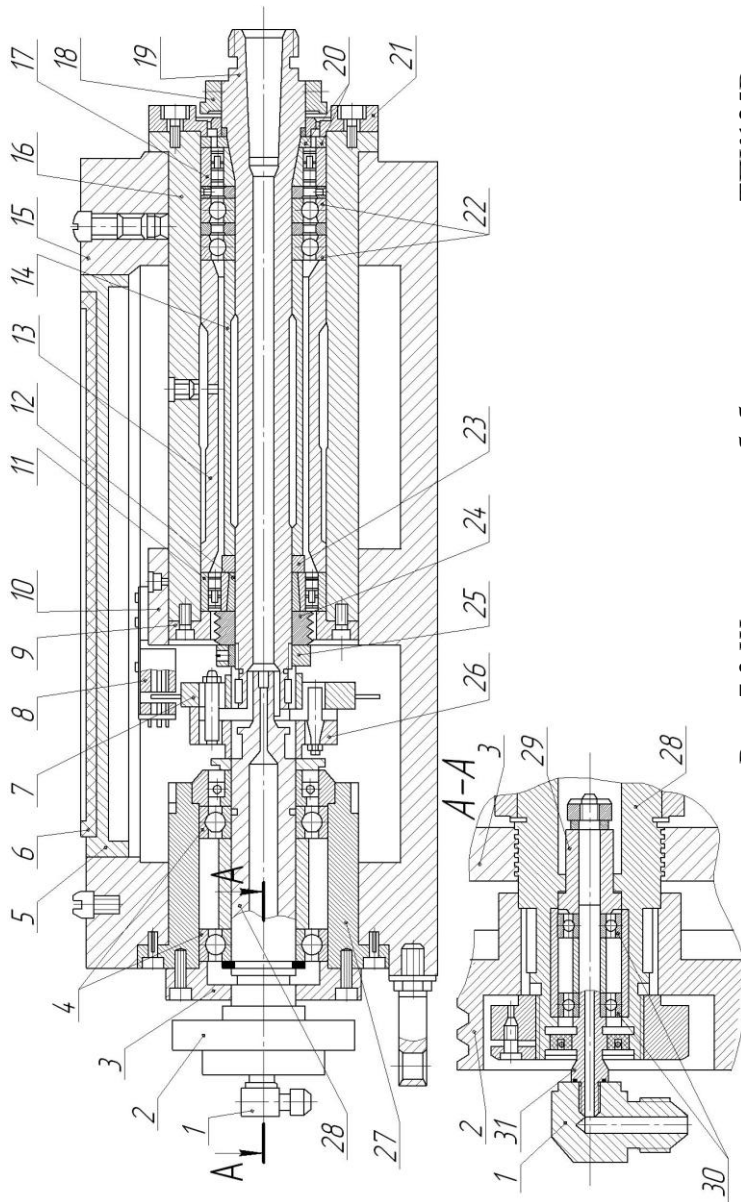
Шпиндельная бабка станка мод. ТПК125В
